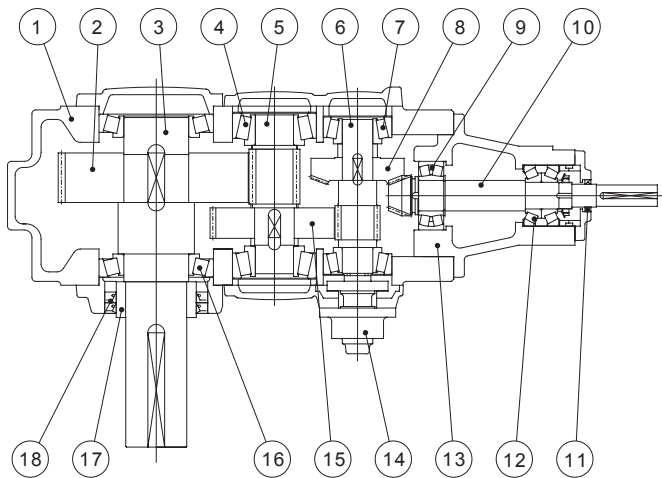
Getriebe mit rechtwinkliger Wellenanordnung
